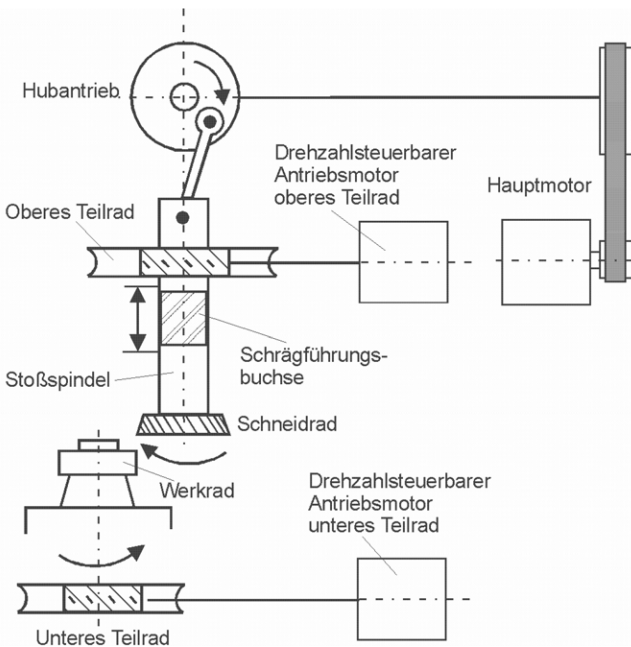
Getriebeschema einer Wälzstoßmaschine mit Einzelantrieben
